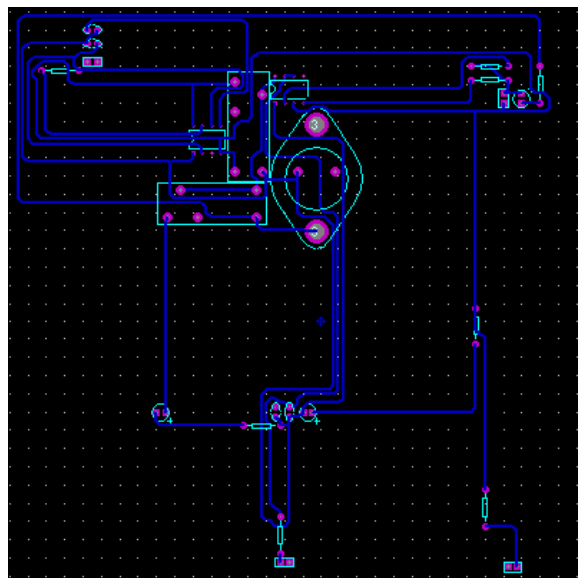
Diseño de placa PCB para el generador de pulsos
